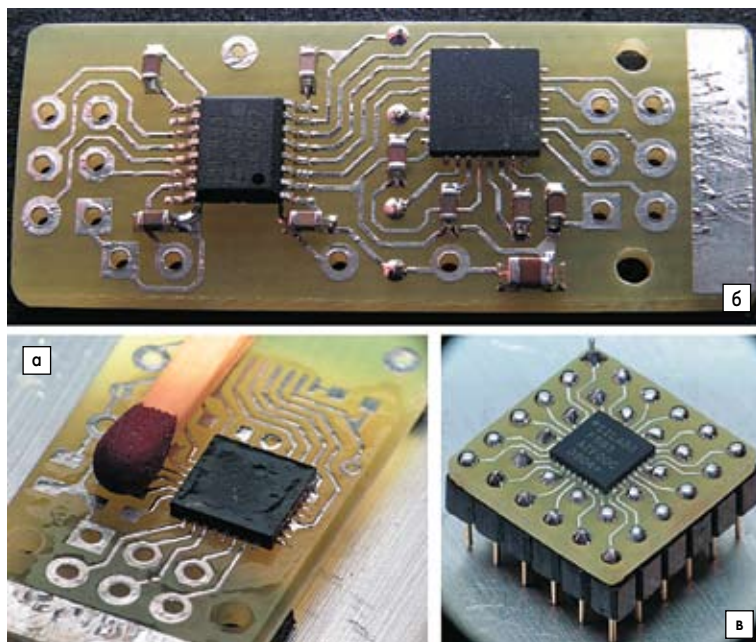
Распайка микросхем в корпусах QFN32 и QSOP16:
